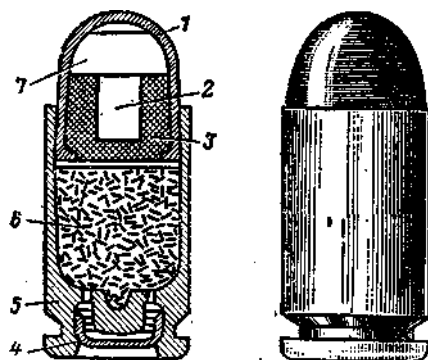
Общий вид 9-мм пистолетного патрона и его устройство: 1 — биметаллическая (плакированная) оболочка; 2 — стальной сердечник; 3 — свинцовая рубашка; 4 — капсюль; 5 — гильза; 6 — пороховой заряд; 7 — пуля
